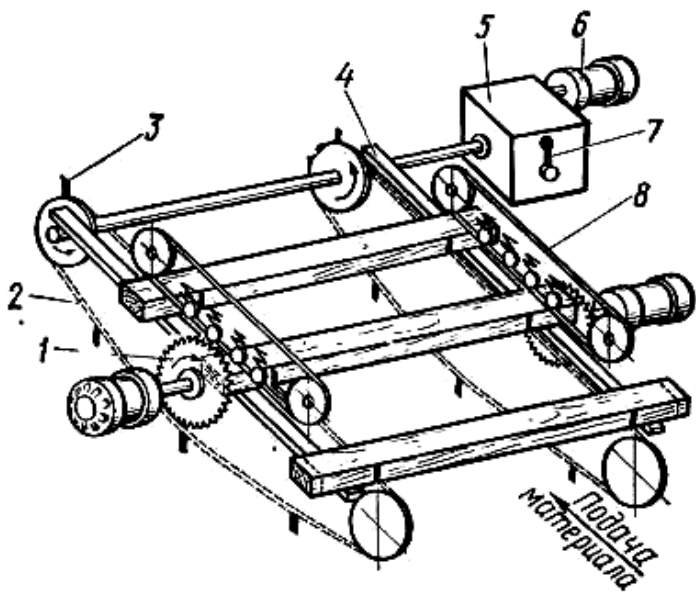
Концевальный двухпильный станок с конвейерной подачей заготовок:
